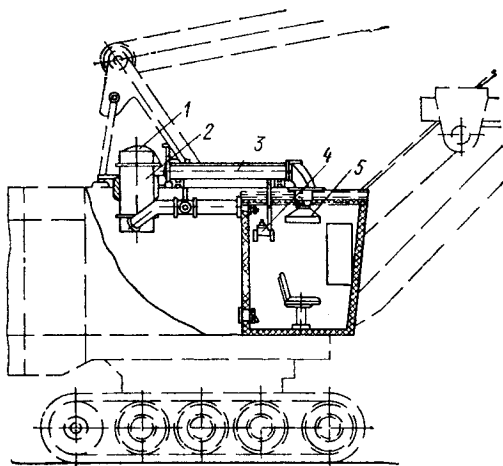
Універсальна фільтровентиляційна установка на екскаваторі
